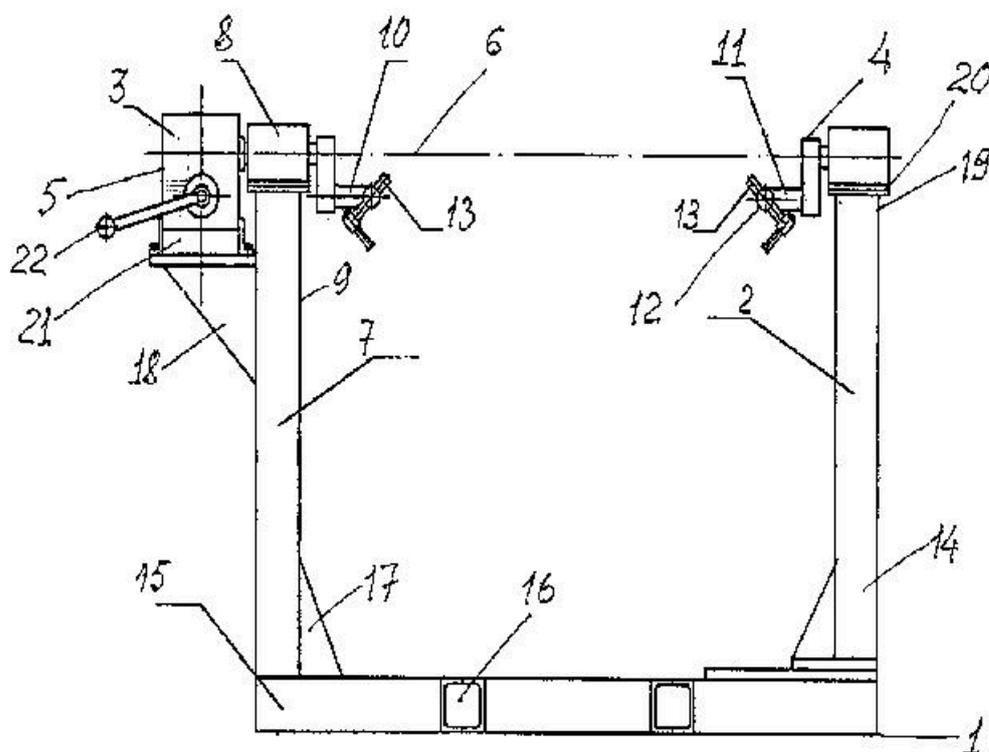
Схема станда для ремонта двигателей вид спереди
